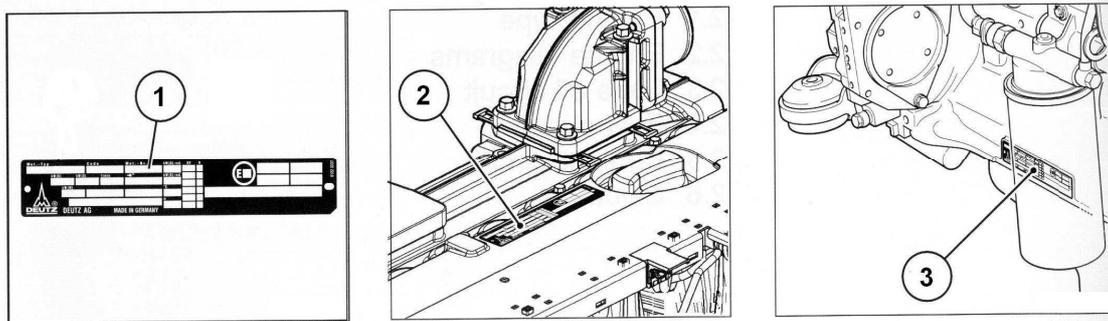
Расположение заводского щитка 1 двигателя DEUTZ (на крышке 2 и с правой стороны блока-картера двигателя 3)
